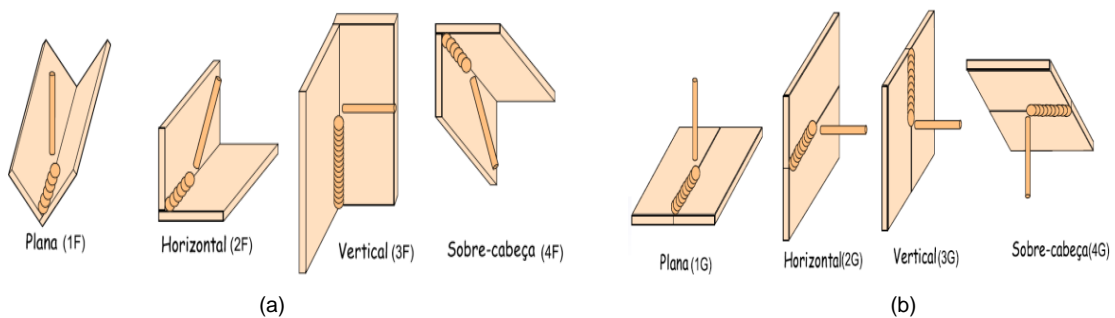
Posições de soldagem para soldas de filete (a) e soldas em tubulações (b). (Fonte: Soldagem: fundamentos e tecnologia / Paulo Villani Marques, Paulo José Modenesi, Alexandre Queiroz Bracarense – 3ª edição atualizada – Belo Horizonte: Editora UFMG, 2009)
